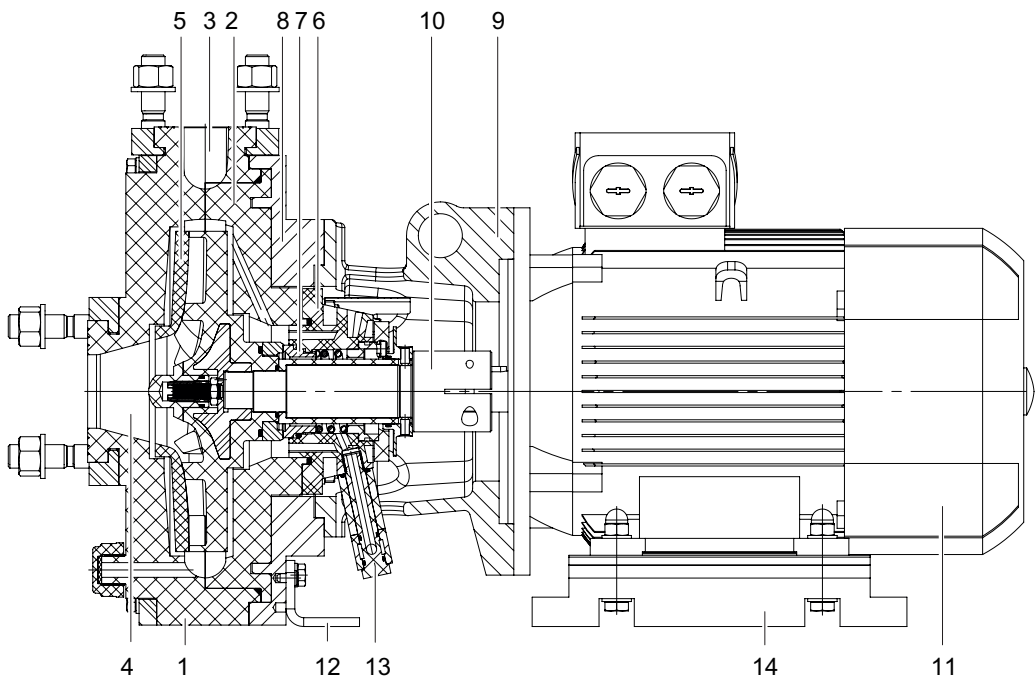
Aufbau (Anschlussvariante Flanschanschluss)
